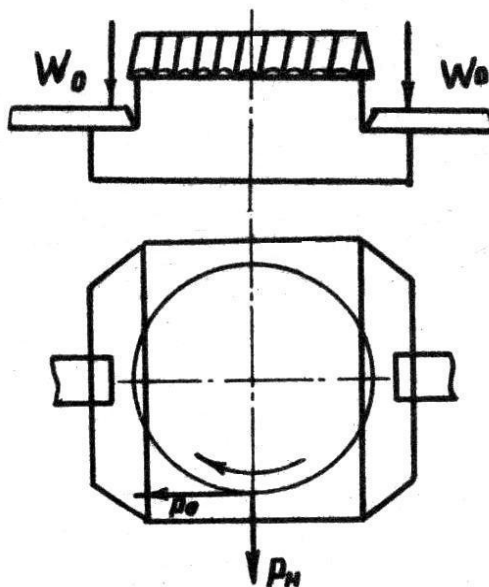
Схема розрахунку сил затиску для фрезерування торцевою фрезею
